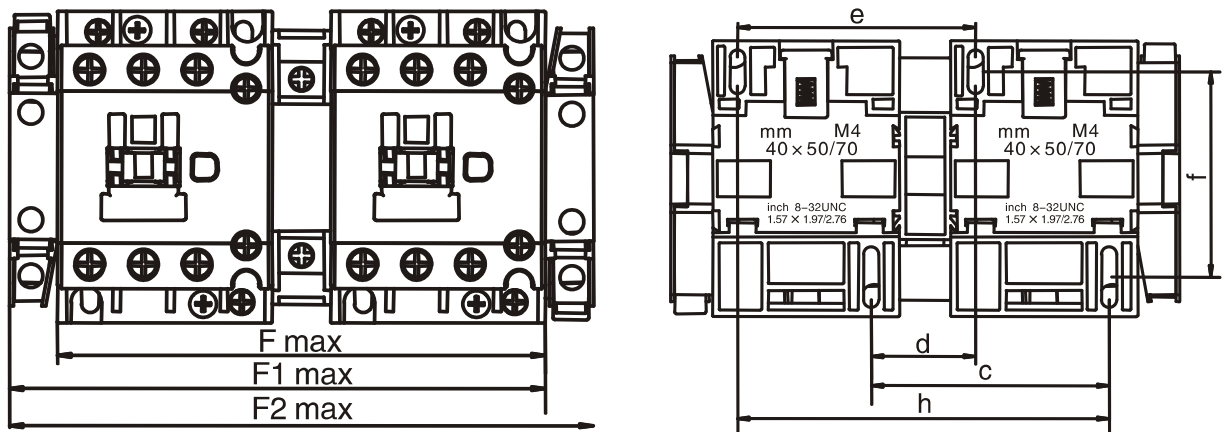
Габаритные и установочные размеры контакторов с реверсивной сборкой на токи 9-38А, мм.
